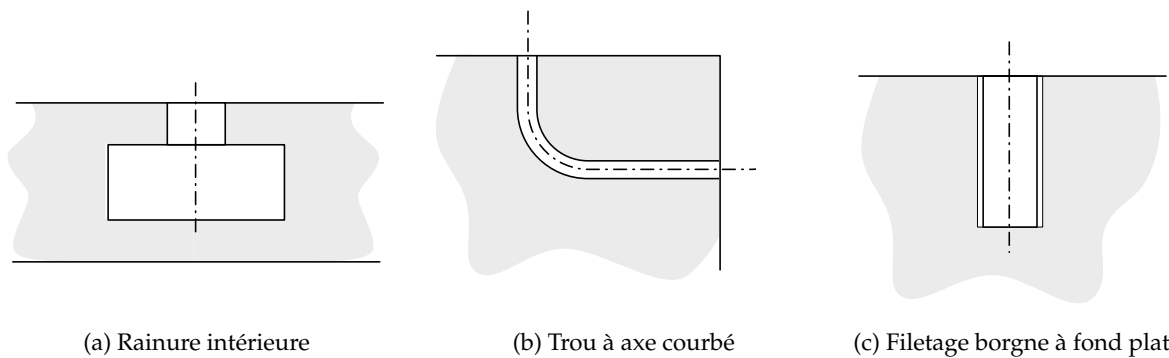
Exemples de pièces non fabricables par usinage (ici en vue de coupe; tirés de [Boothroyd et coll., 2001]).
